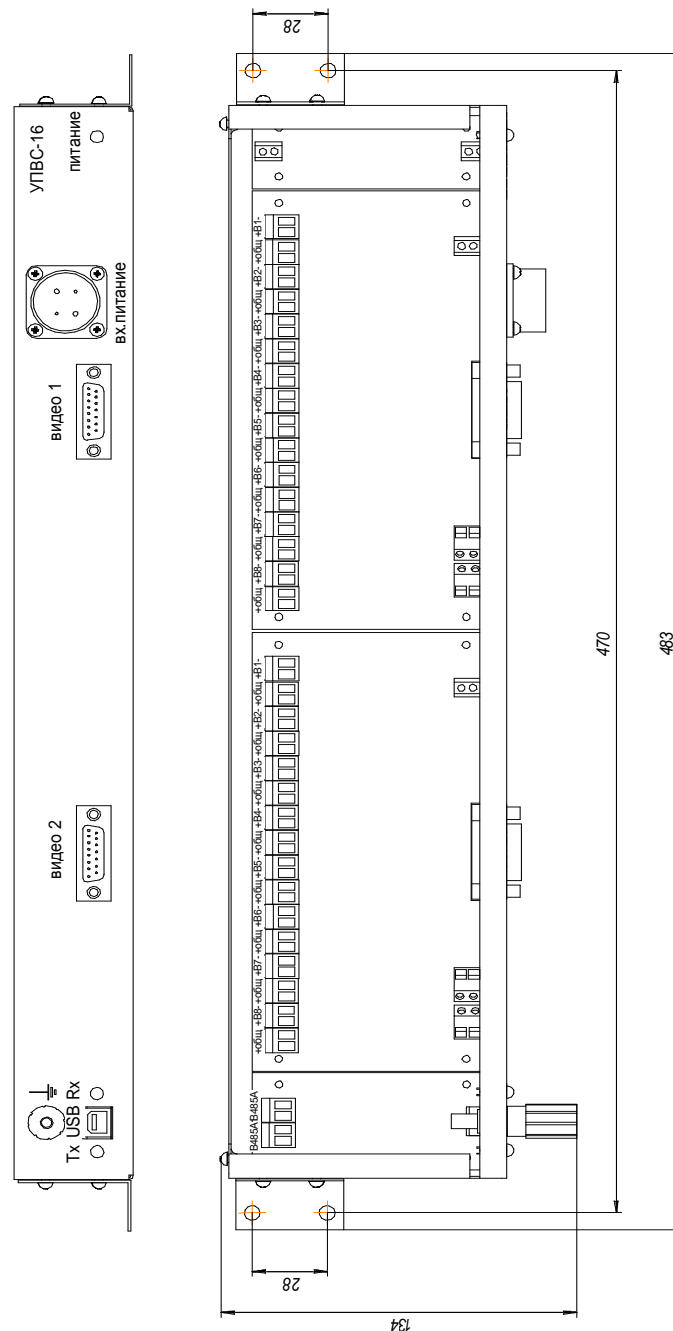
Вид со стороны разъёмов и вид без крышки УПВС-16
